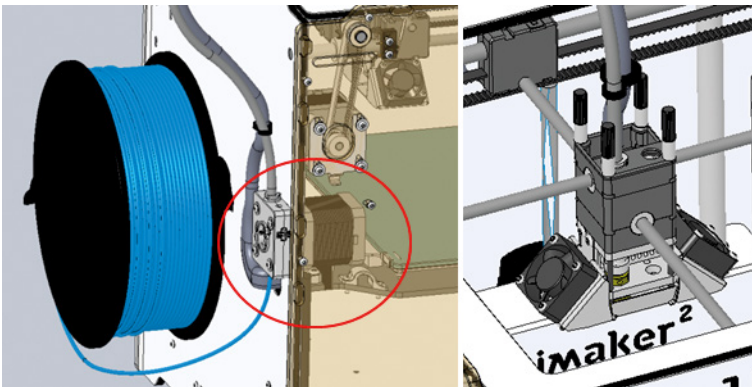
Bowden-Extruder auf der Rückseite des 3D-Druckers (links); Hotend eines 3D-Druckers mit Bowden-Extruder (rechts)
